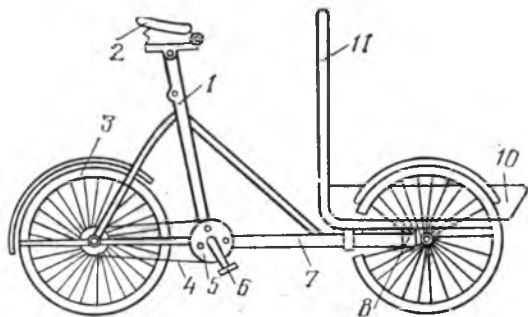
1 — каркас; 2 — седло; 3 — задние колеса; 4 — цепь; 5 — звездочка; 6 — педали; 7 — поворотный кронштейн; 8 — ведущий шарнир; 9 — рама тележки; 10 — кузов; 11 — руль; 12 — ограничитель поворота; 13 — ось колес
